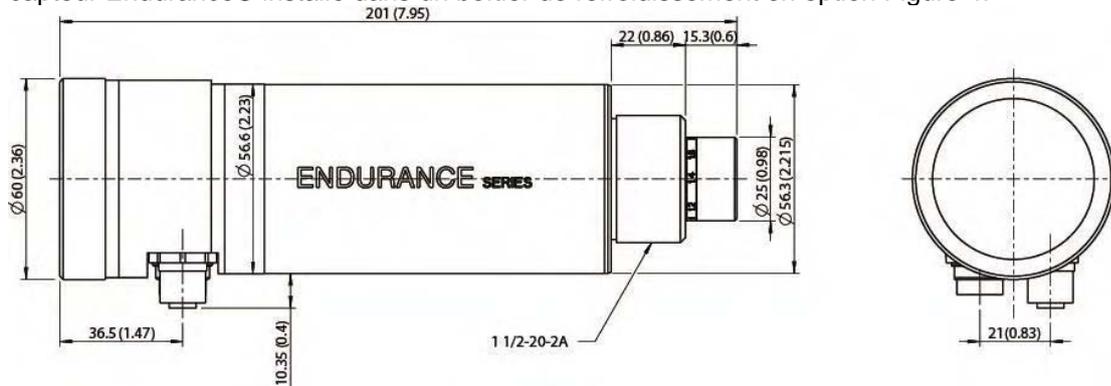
Dimensions d'un capteur Endurance® avec boîtier standard
